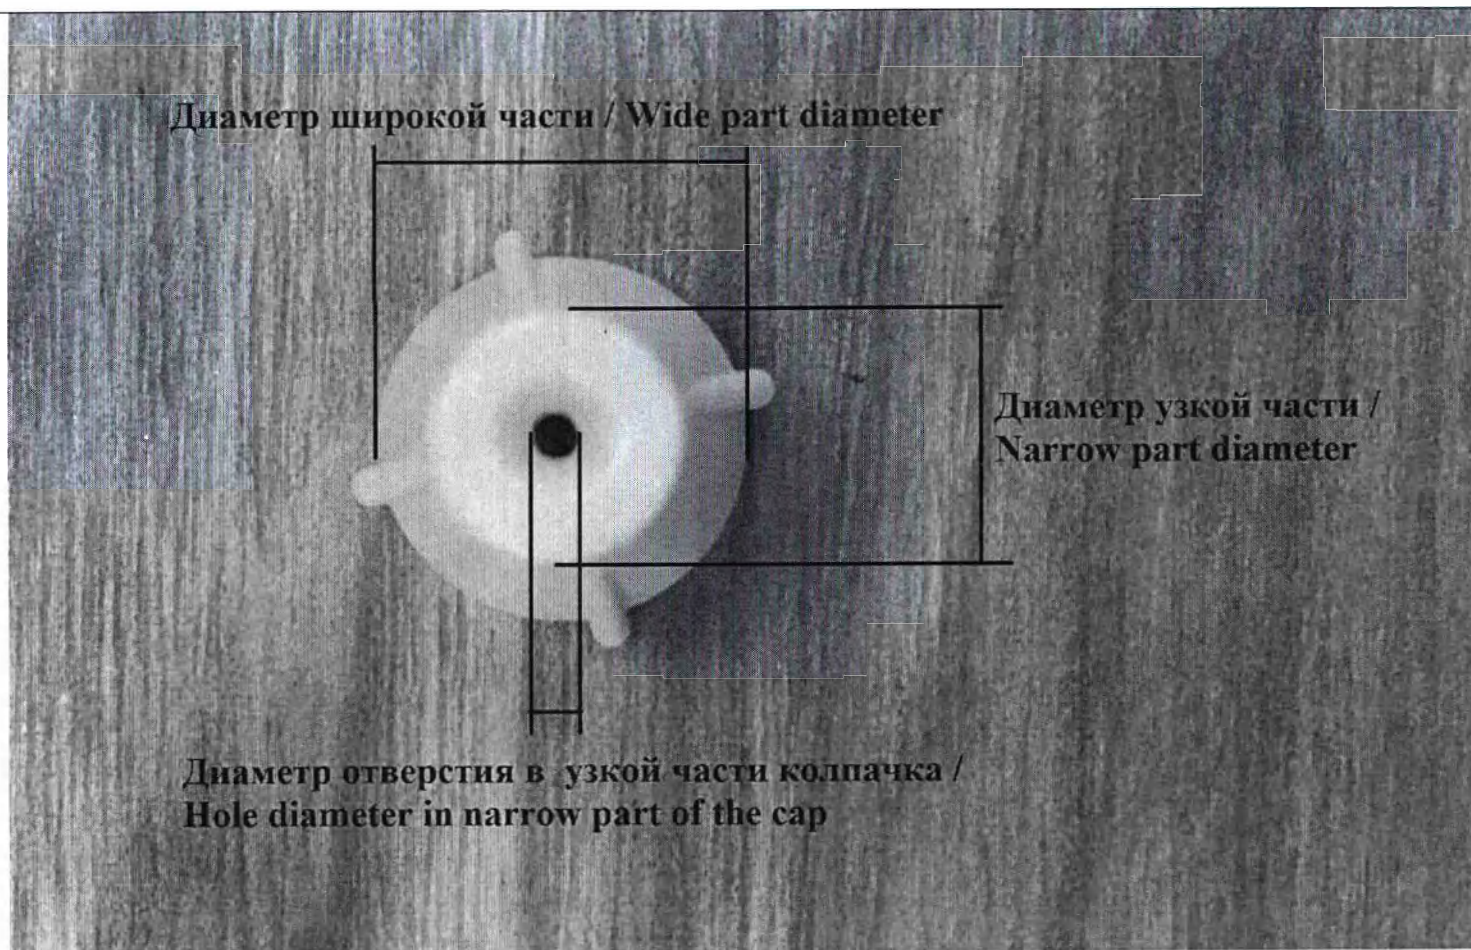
Поворотное устройство / Picture 4 Torque device
